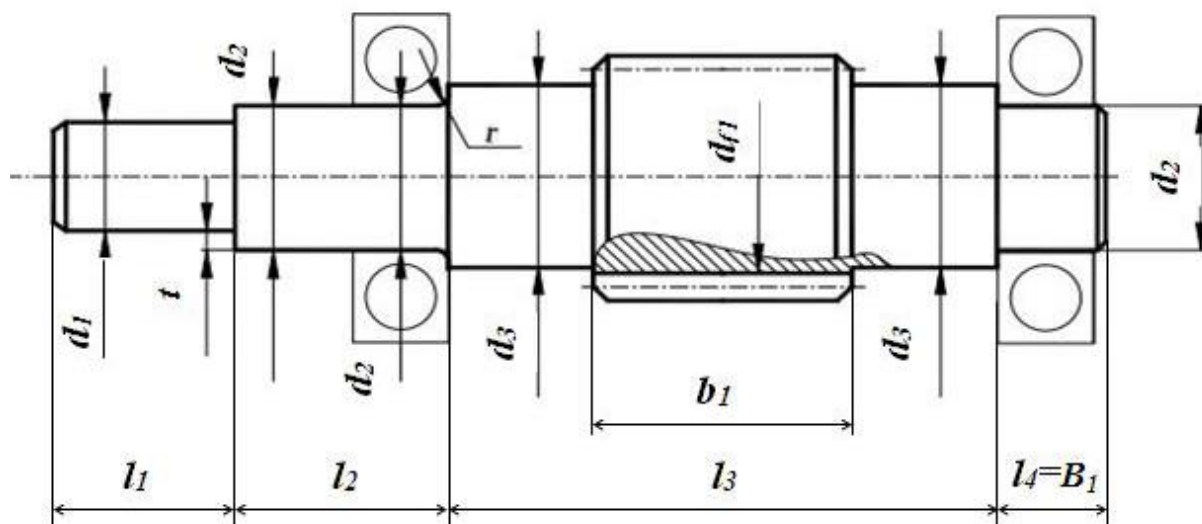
Схема ведущего быстроходного вала (вал-шестерня)
